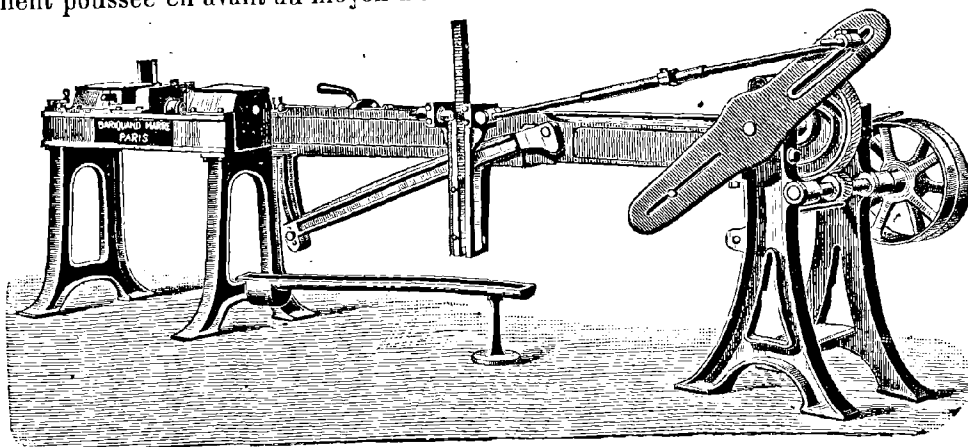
Machine à rayer les canons de fusils de MM. Bariquand et Marre.
